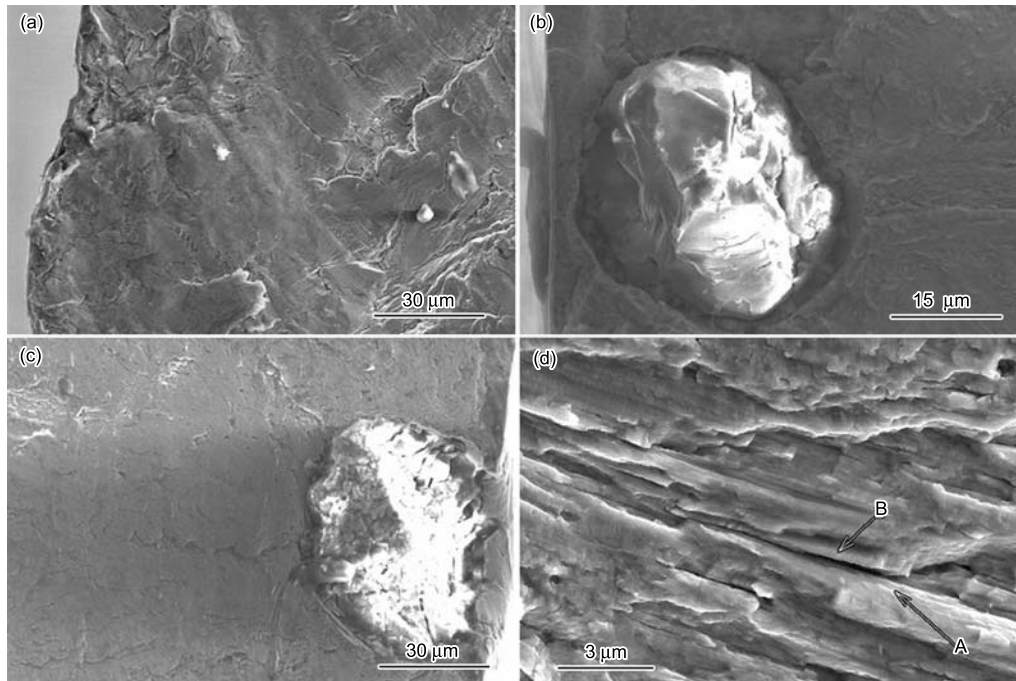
实验钢疲劳断口裂纹源区及扩展区形貌
